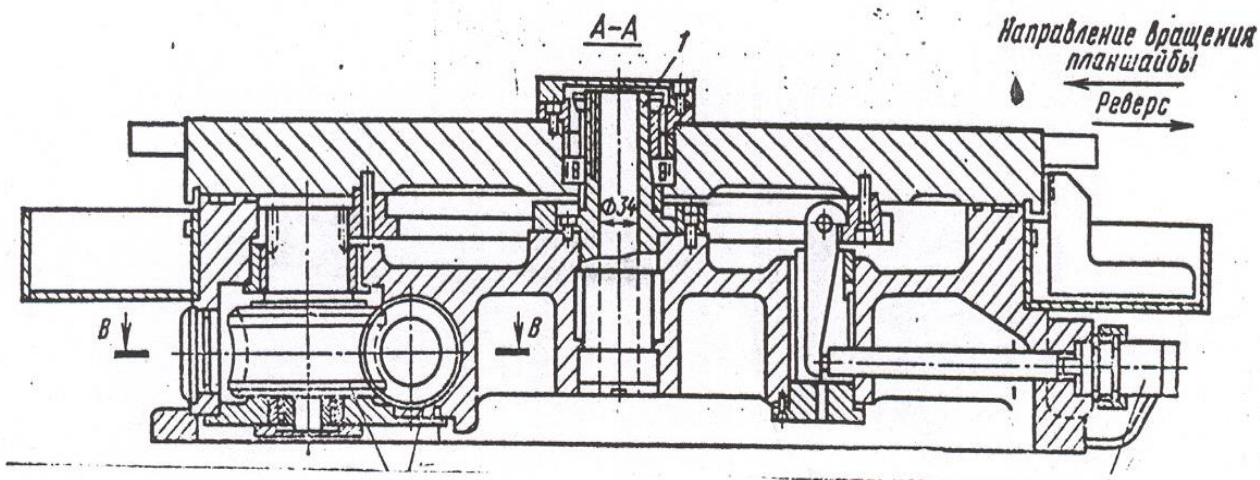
Разрез поворотного – делительного стола агрегатного станка
